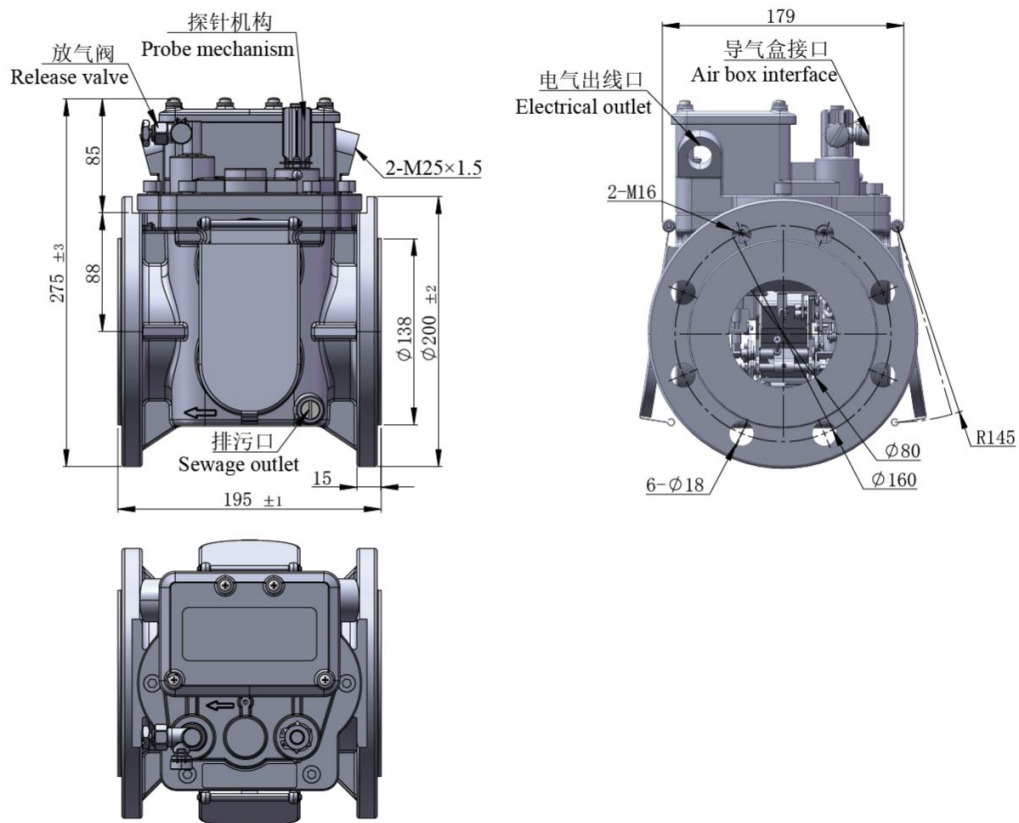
QJ9-80TH-04 气体继电器（圆法兰 8 孔）外形尺寸
